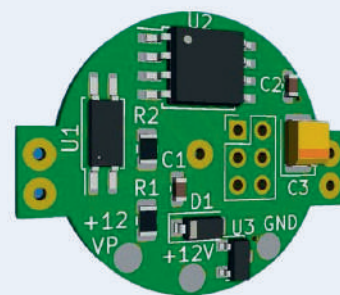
Aperçu en 3D de la platine dessiné par l'auteur.
